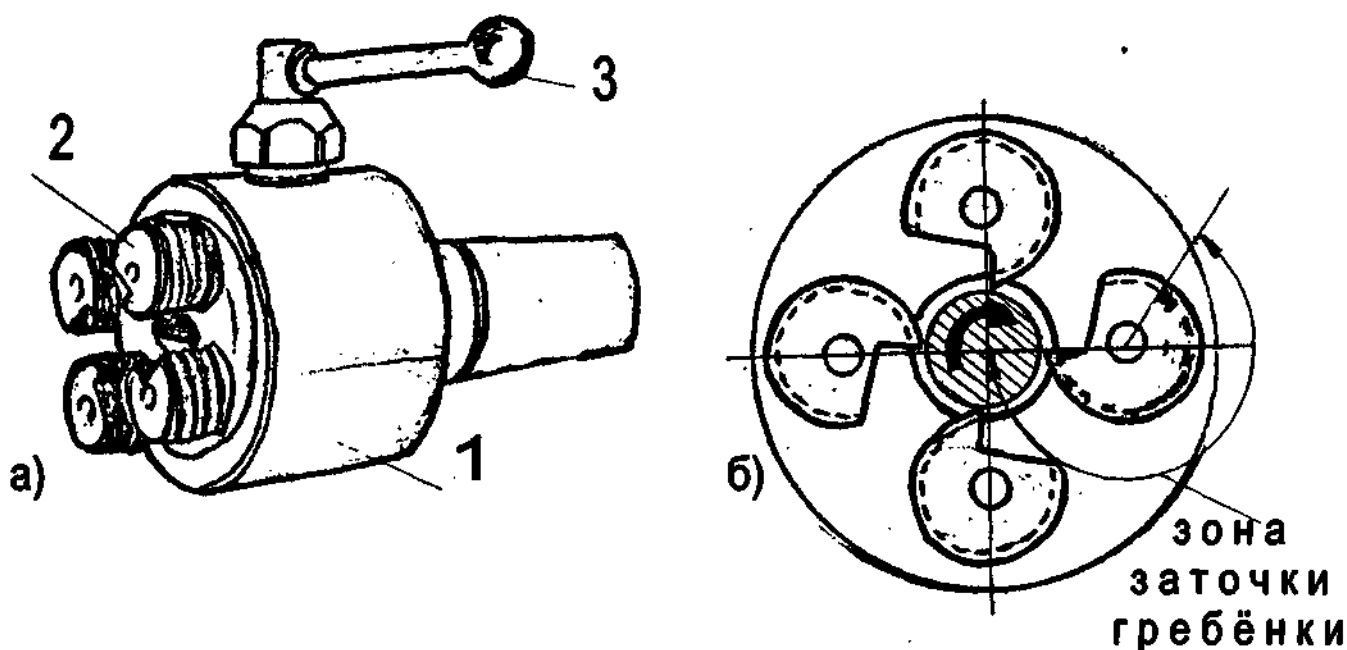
Самораскрывающаяся резьбонарезная головка.
